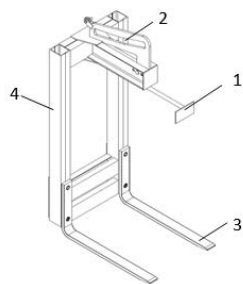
Захватное устройство для поддонов: 1 – упор; 2 – каретка; 3 – вилы; 4 – рама
